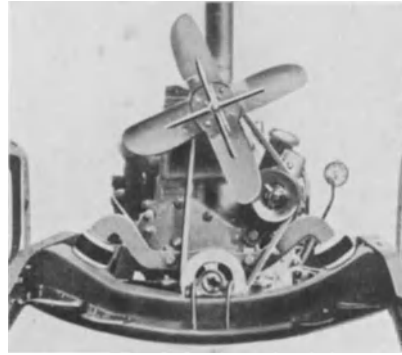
Elastische Lagerung eines Kraftwagenmotors mit druckbeanspruchten Gummifedern.
